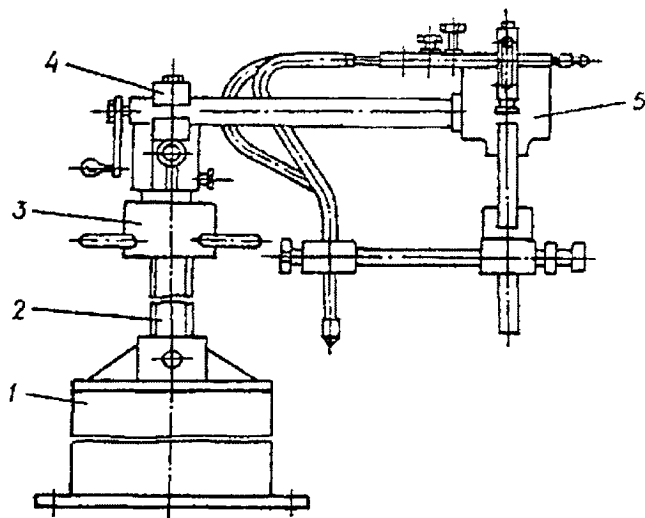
Стационарний пристрій СУ-1М для газополуменового вирізування отворів під штупери в трубах: 1 — рама; 2 — гвинт; 3 — маховик підймання; 4 — кронштейн; 5 — синусний механізм
